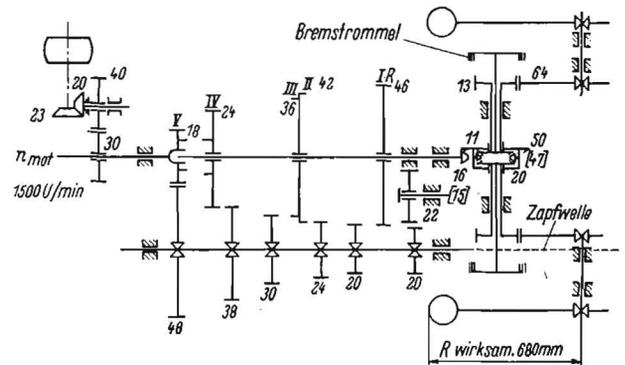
Getriebeschema (die in Klammern angegebene Zähnezahl gilt für Zerolverzahnung, siehe Tabelle 1)
